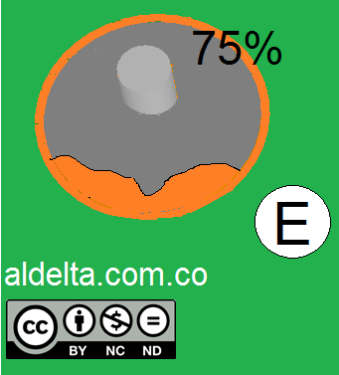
Porcentaje del área del pad mojado de soldadura THT en el lado abajo o origen de la soldadura según la IPC 610. Autoría propia.
